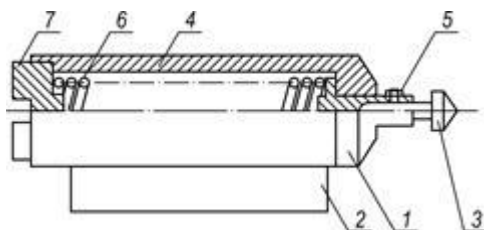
Пристосування для нанесення регулярного мікрорельєфу на бічну поверхню голки розпилювача дизельної форсунки
